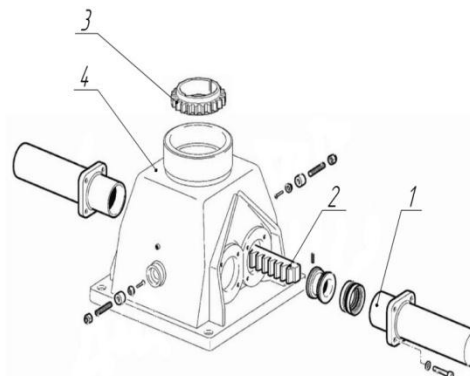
Опорно-поворотний пристрій на основі двох гідроциліндрів та рейкової пари.
